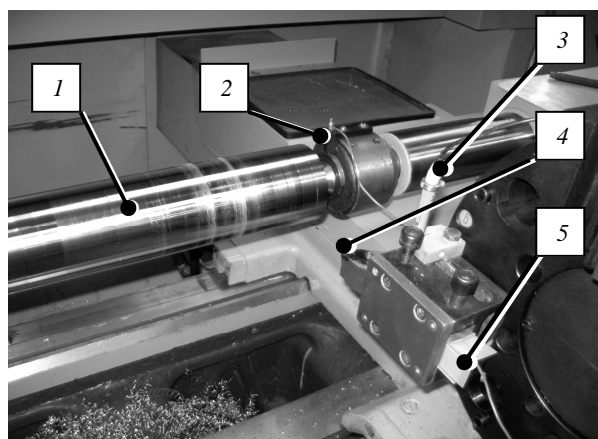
Рабочая зона станка: 1 – обрабатываемая заготовка; 2, 5 – клеммы естественной термопары; 3 – датчик измерения силы резания; 4 – резец
